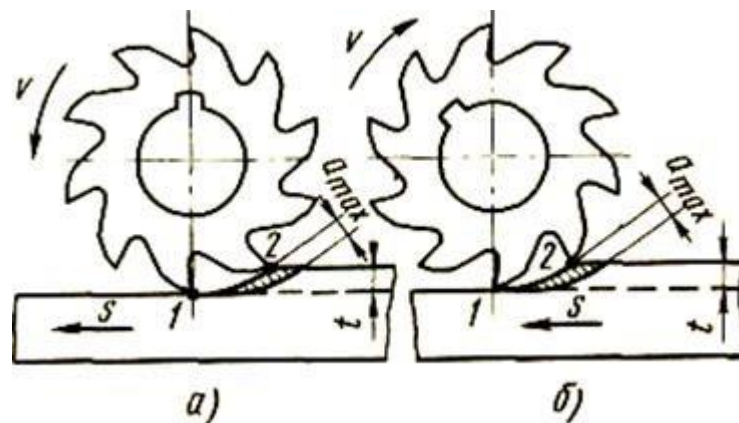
Схеми зустрічного (а) і попутного (б) фрезерування.
